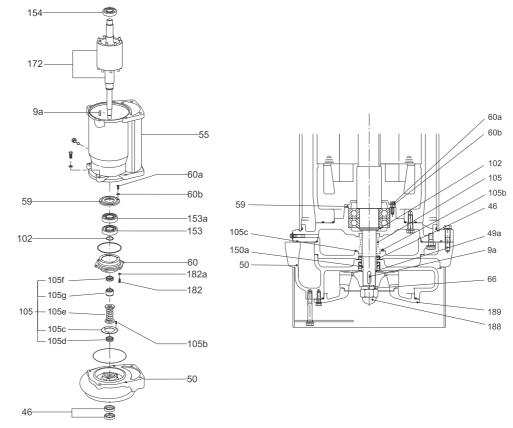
Демонтаж торцевого уплотнения и подшипников
